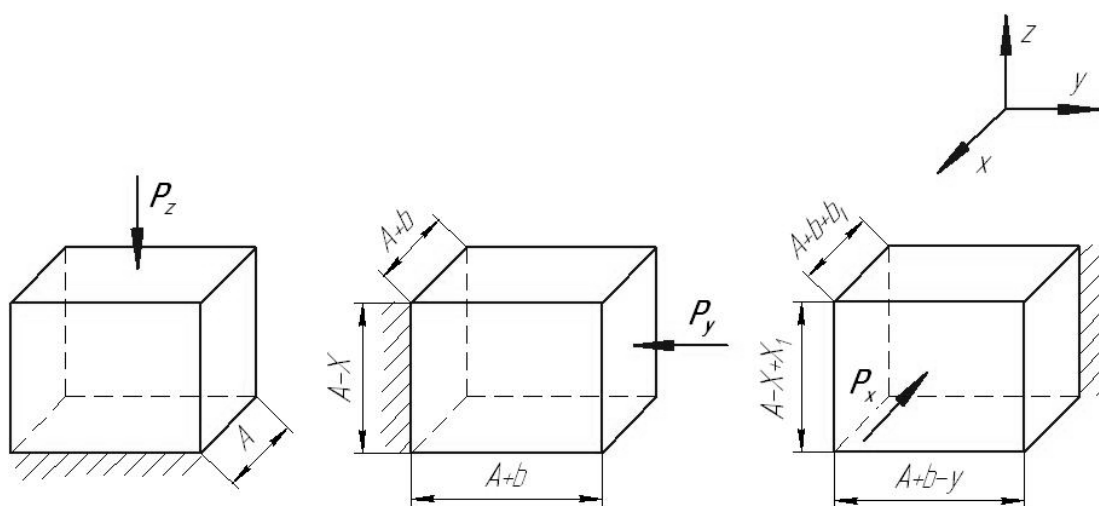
Способ всестороннейковки кубической заготовки
